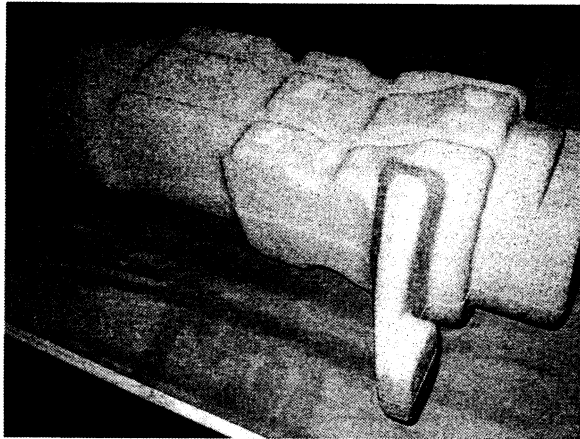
Сплошной стержень отливки «Рукав полуоси» № 1221-2407018Б/01Б
